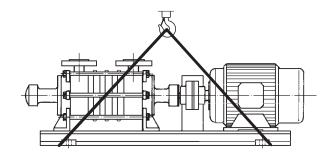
Fixer l'engin de levage à l'unité de pompage avec plaque de fondation
